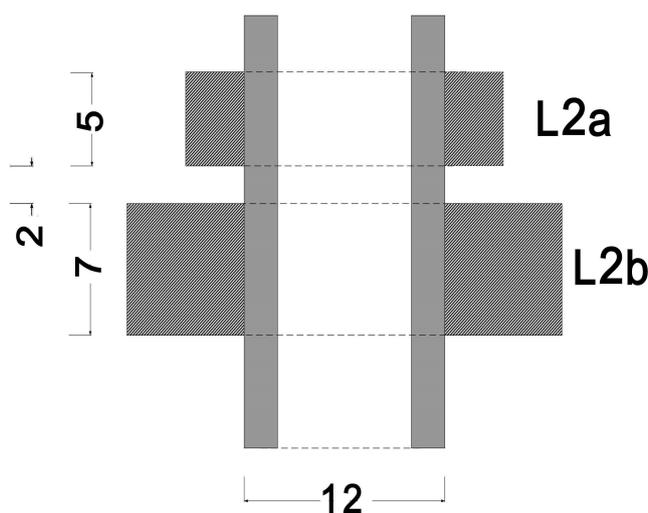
Bobina oscillatrice ( dimensioni in mm )
